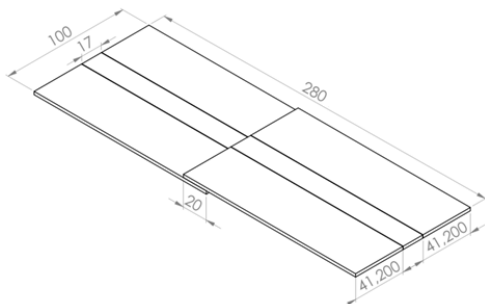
Dimensões, em milímetros, das amostras soldadas.
